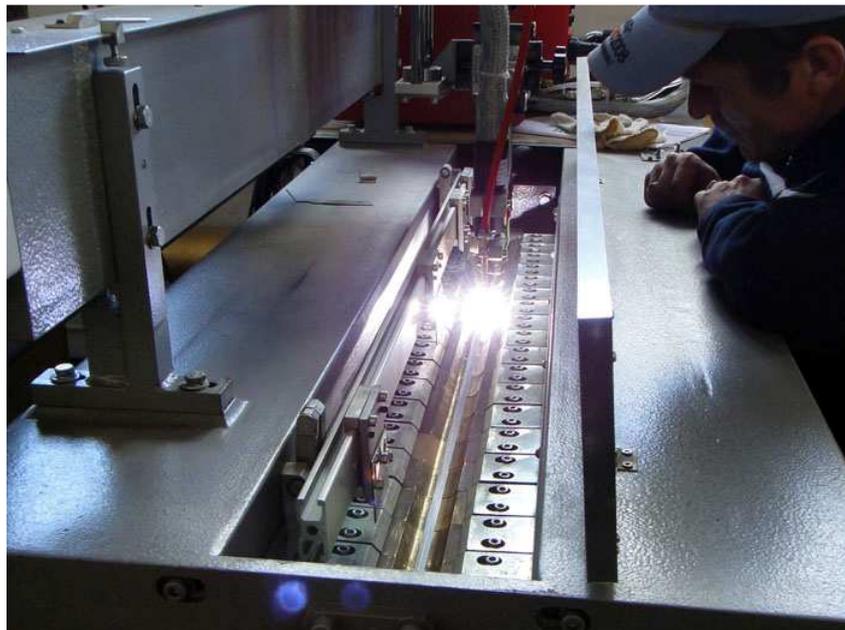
Сварочный аппарат для обратного формирования шва
